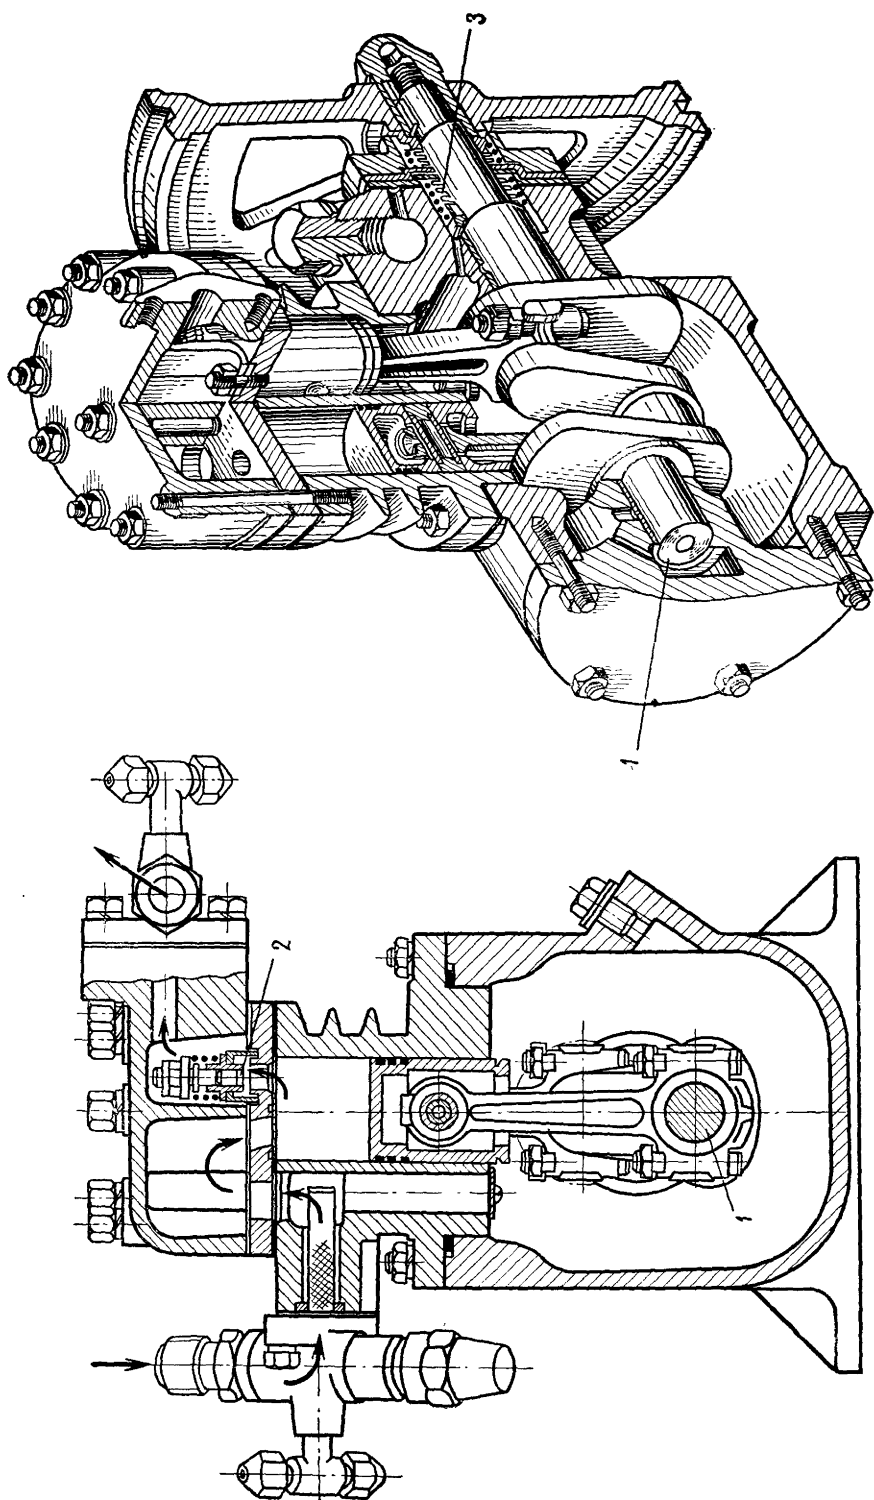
Открытый феоновый поршневой компрессор 2ΦВ4.
